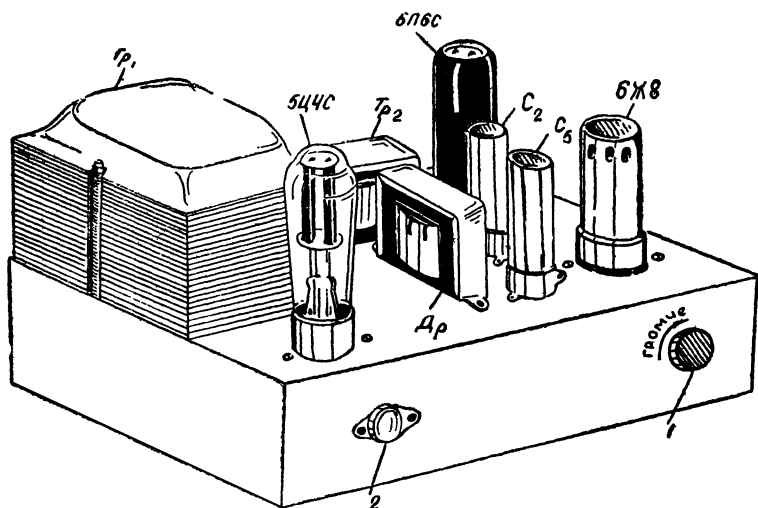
Внешний вид усилителя для проигрывания пластинок:
